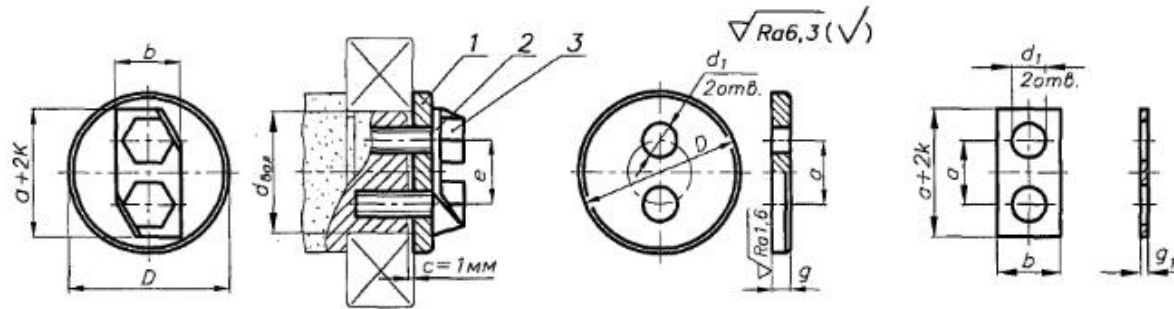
Закрепление подшипника на валу с использованием концевой шайбы:
